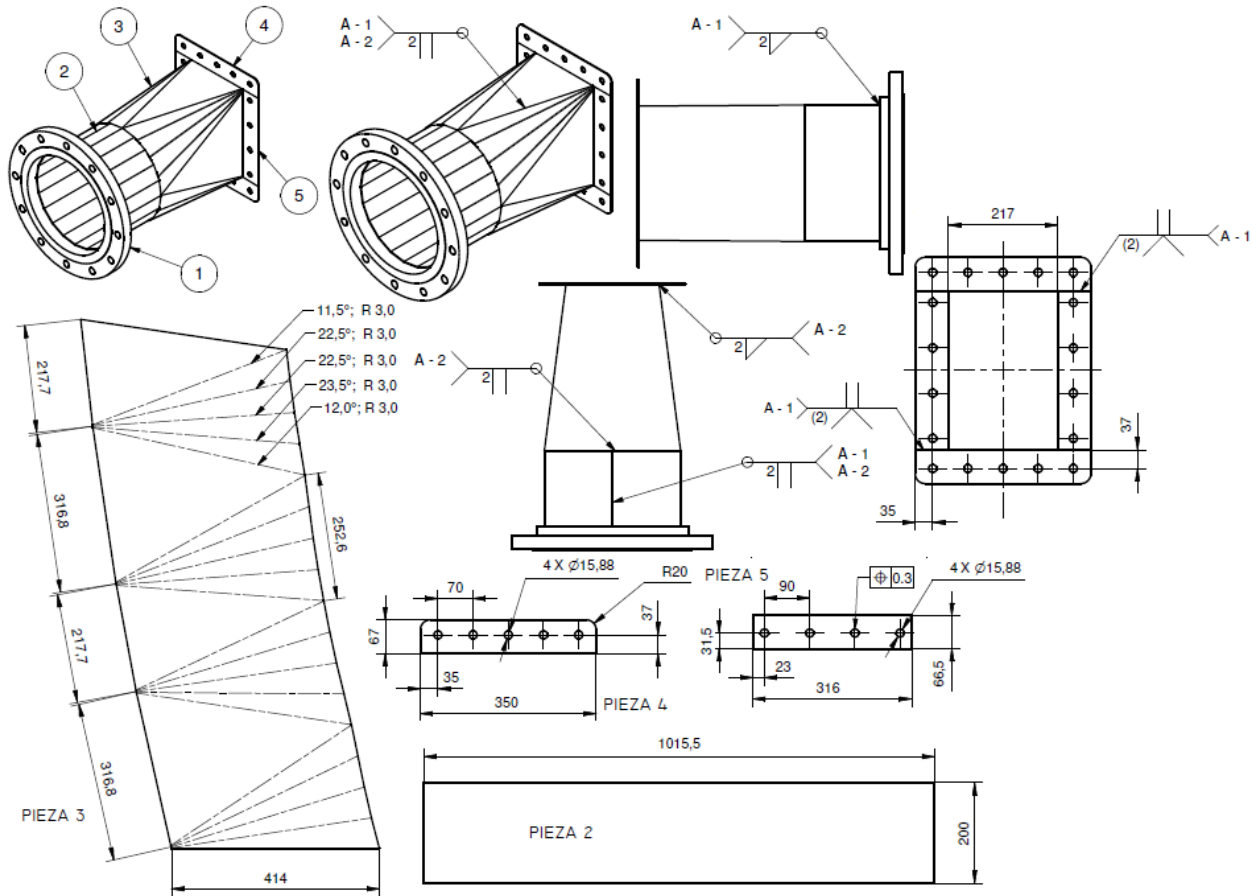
Plano de ensamble soldado: Transición. Detalle de componentes, incluyendo brida.
